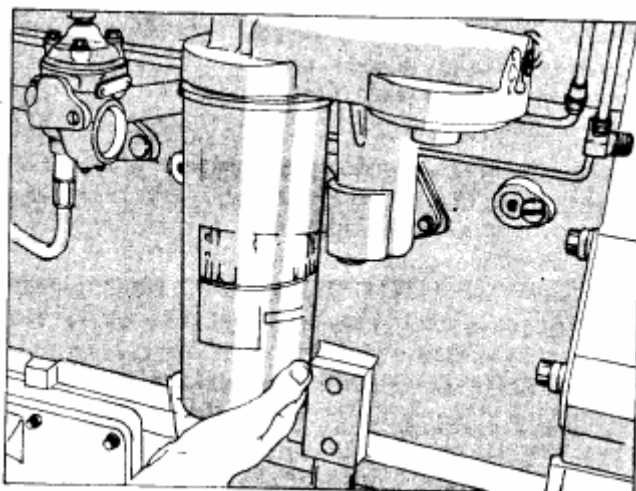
(OM1016L). Установка патрона фильтра смазывающего масла
